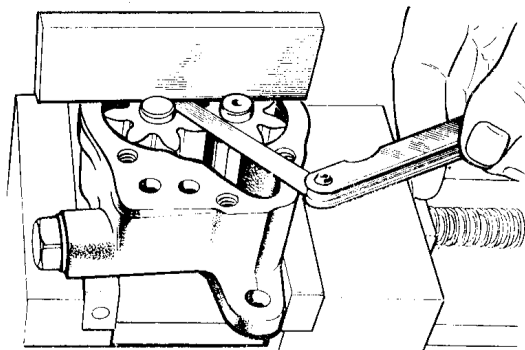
Проверка зазора между торцами шестерен и плоскостью корпуса насоса
